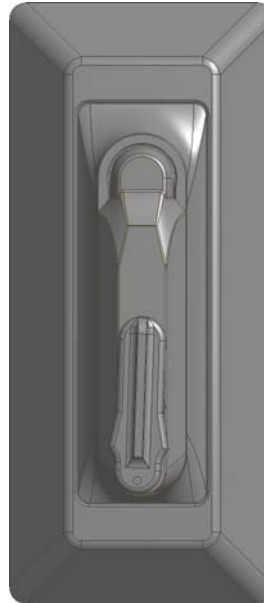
Schwenkhebel mit Profilhalbzylinder
